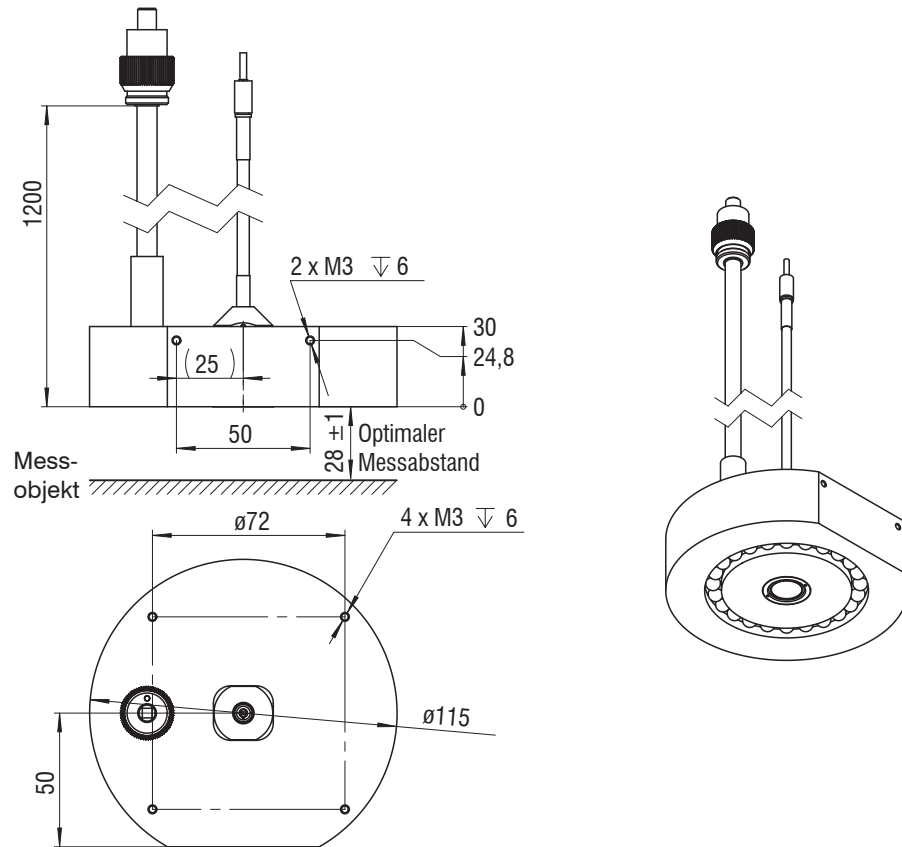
Maßzeichnung Ringsensor FCS-X-ACS2-R45/0-28-XXXX
